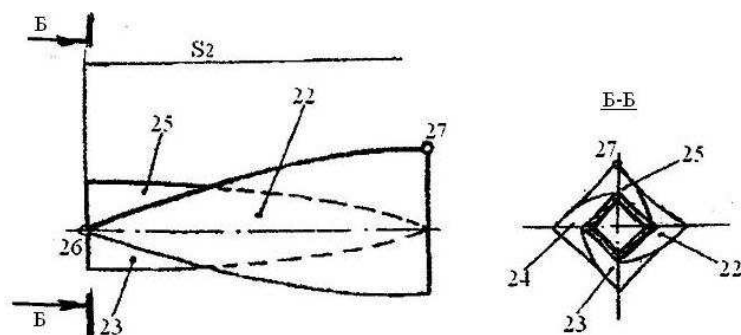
Часть корпуса вращающейся печи для приготовления цементного клинкера с четырьмя винтовыми ребрами (22, 23, 24, 25- трапециевидные листы, 26-27- одно из четырех винтовых ребер)
